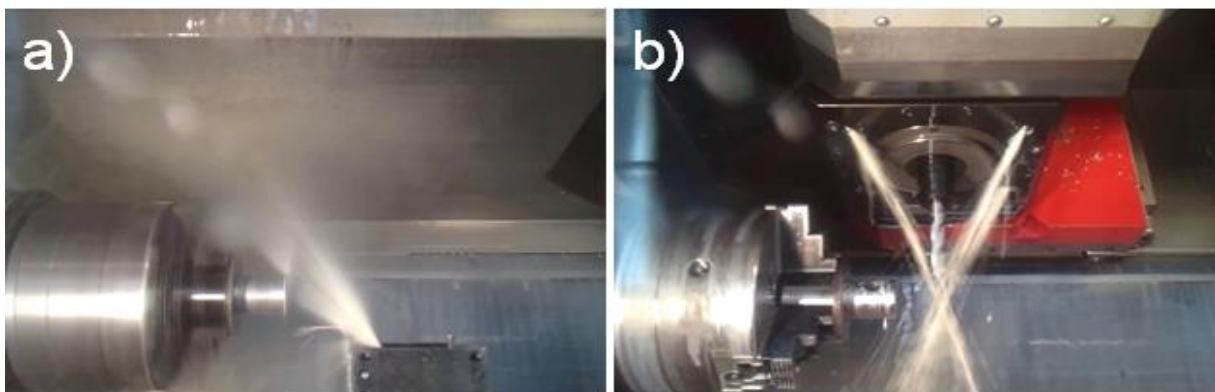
Kühlmittelaustritt a) Werkzeugwender b) Fräsblock
